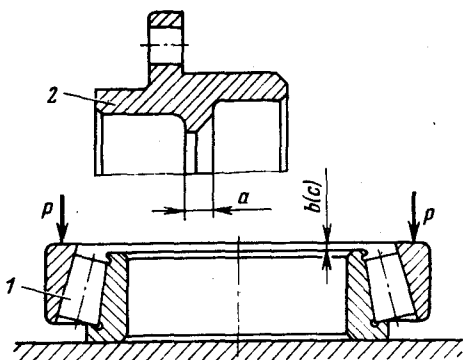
Размеры для определения толщины регулировочной шайбы:
